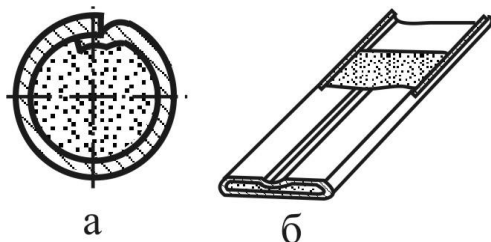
Конструкции порошковой проволоки (а) и ленты (б)
